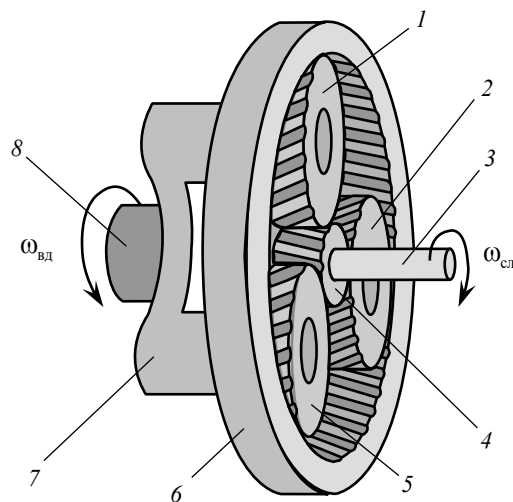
Планетарна зубчаста передача: 1, 2, 5 — сателіти; 3 — вхідний вал; 4 — центральна (сонячна) шестерня; 6 — зубчасте колесо; 7 — водило; 8 — вихідний вал ($\omega_{сл}$ — кутова швидкість обертання сонячної шестерні; $\omega_{вд}$ — кутова швидкість обертання водила планетарної передачі)
